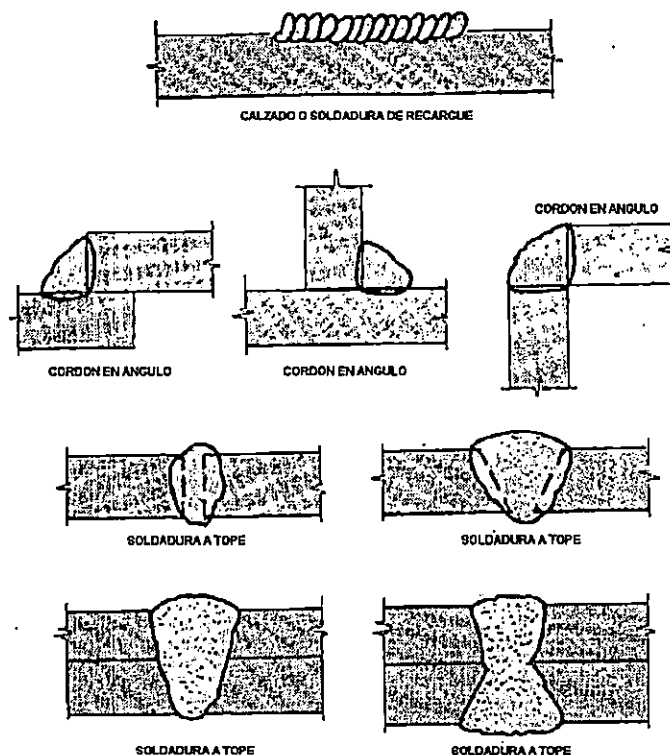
Diferentes tipos de soldaduras.
